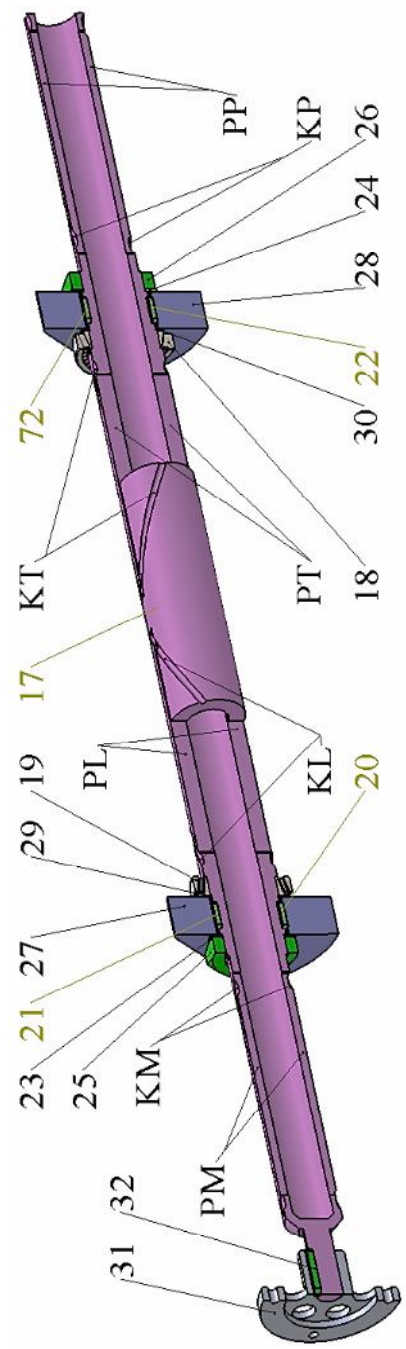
Конструкція приводного валу з нерухомими дебалансами
